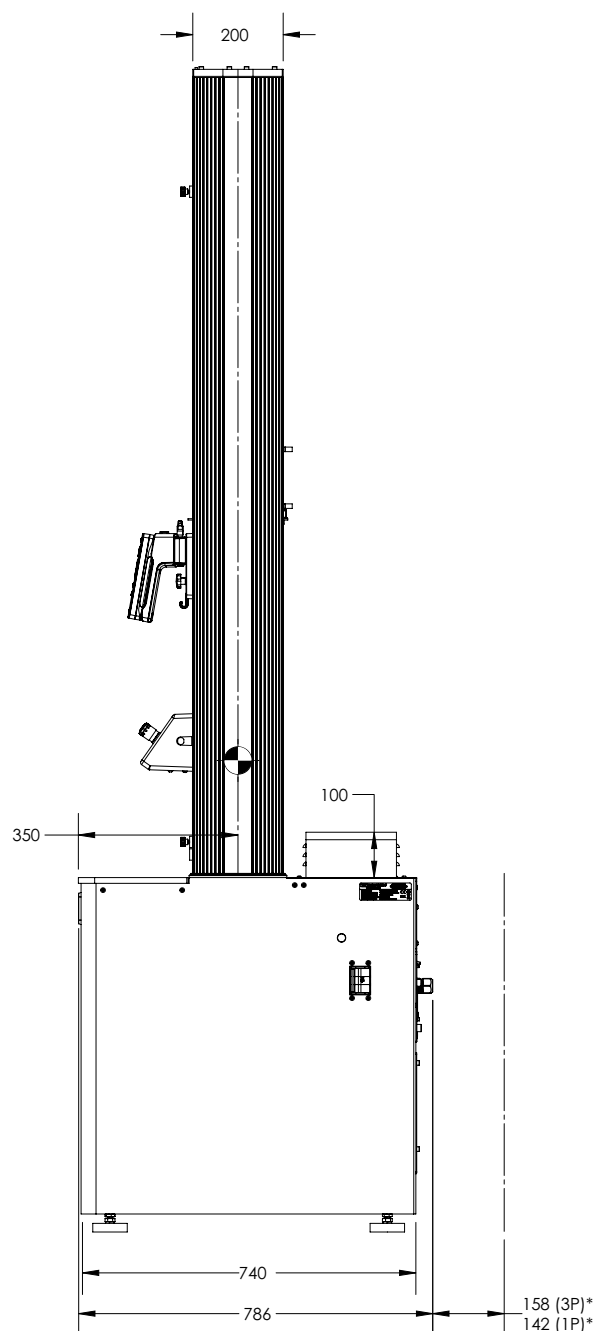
68FM-300 Dimensions du bâti – vue latérale
